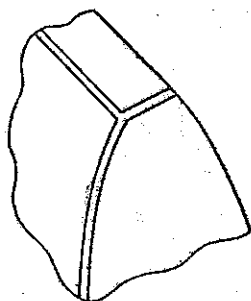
Образование фасок или скруглений на продольных и торцовых кромках зубьев
